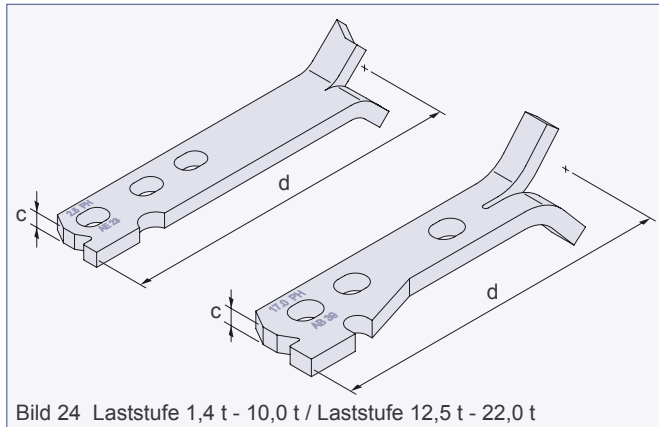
Laststufe 1,4 t - 10,0 t / Laststufe 12,5 t - 22,0 t
